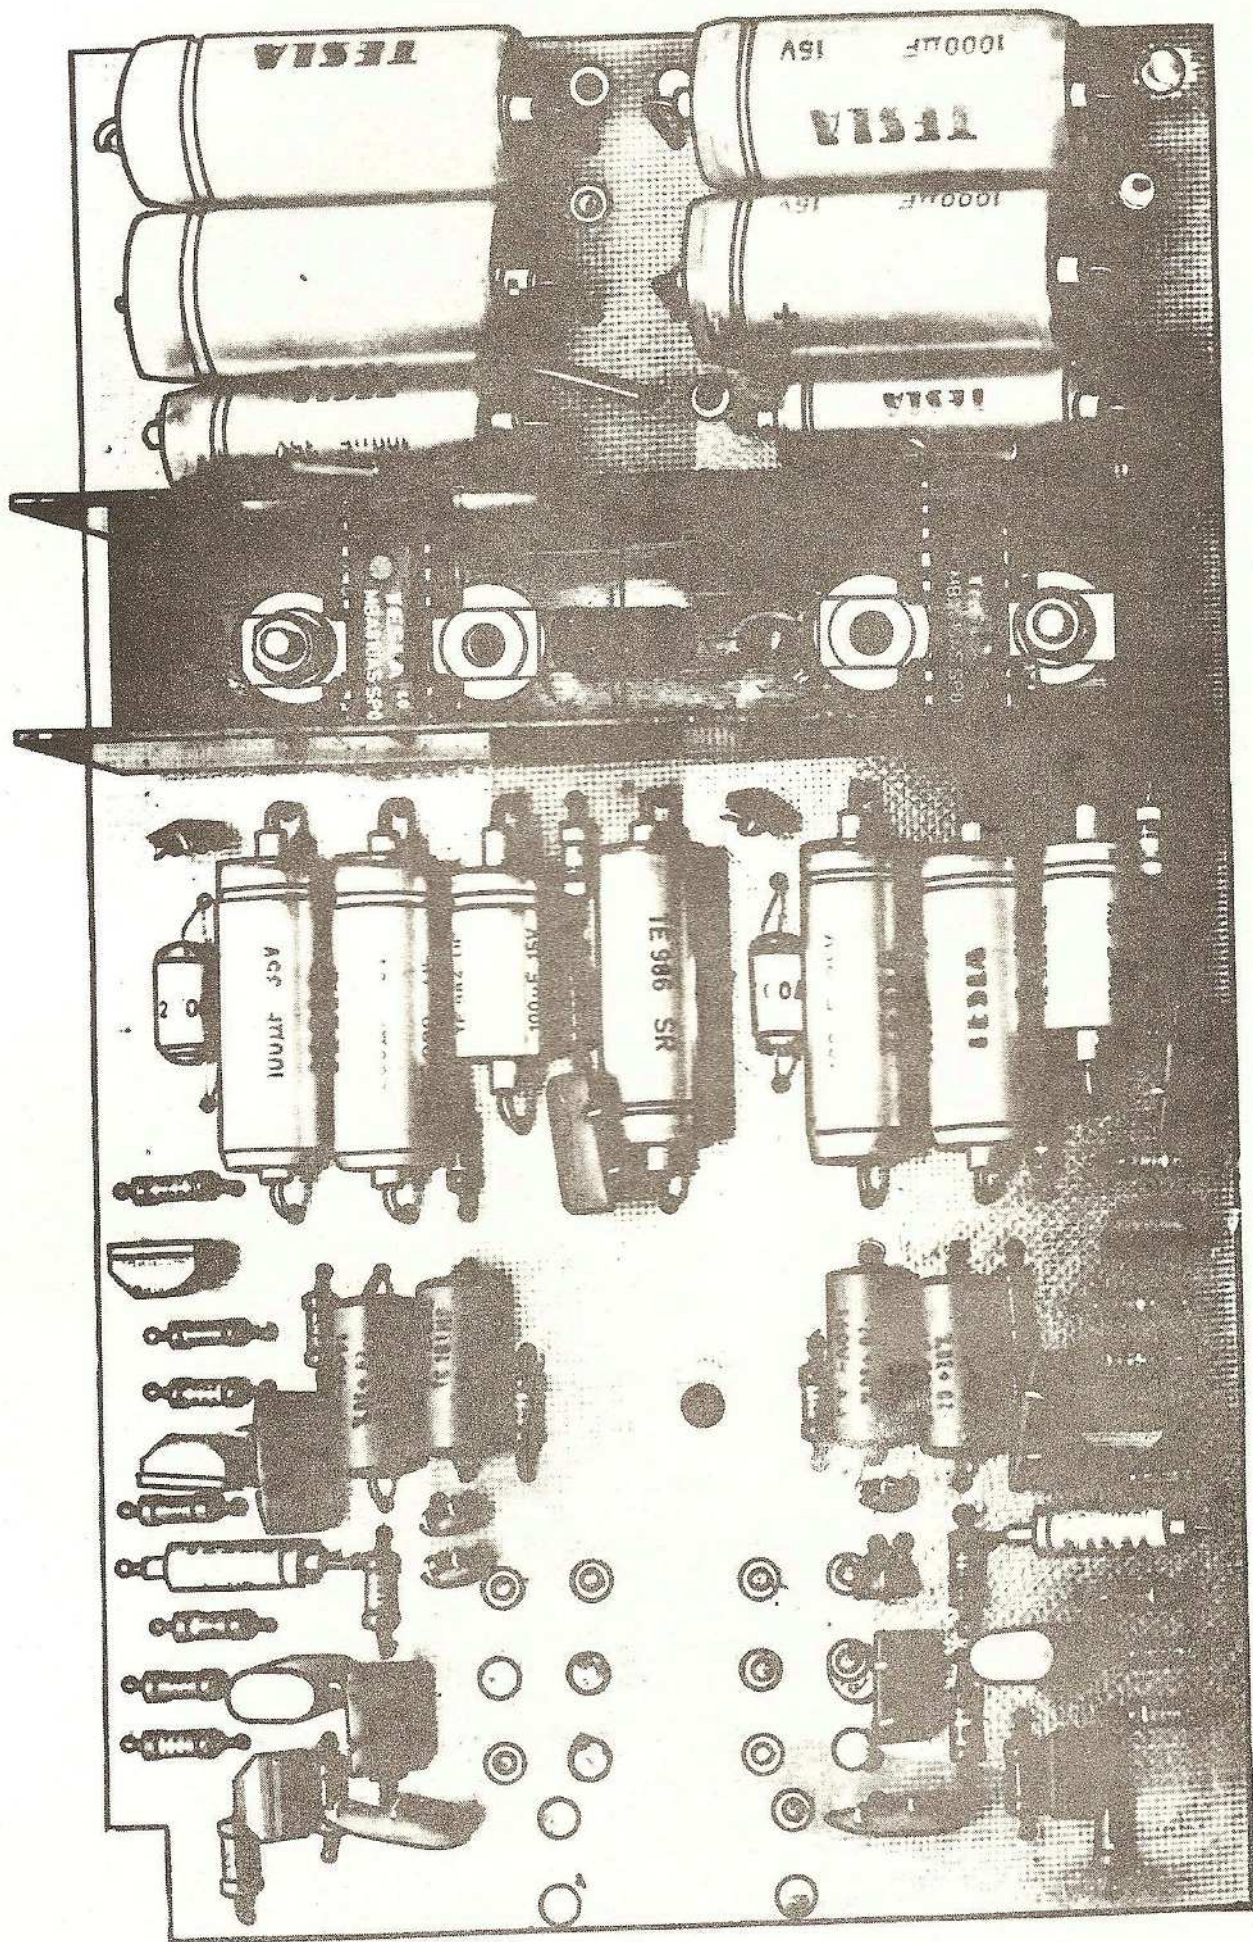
Deska koncového zesilovače B100A (ze strany spojů)
